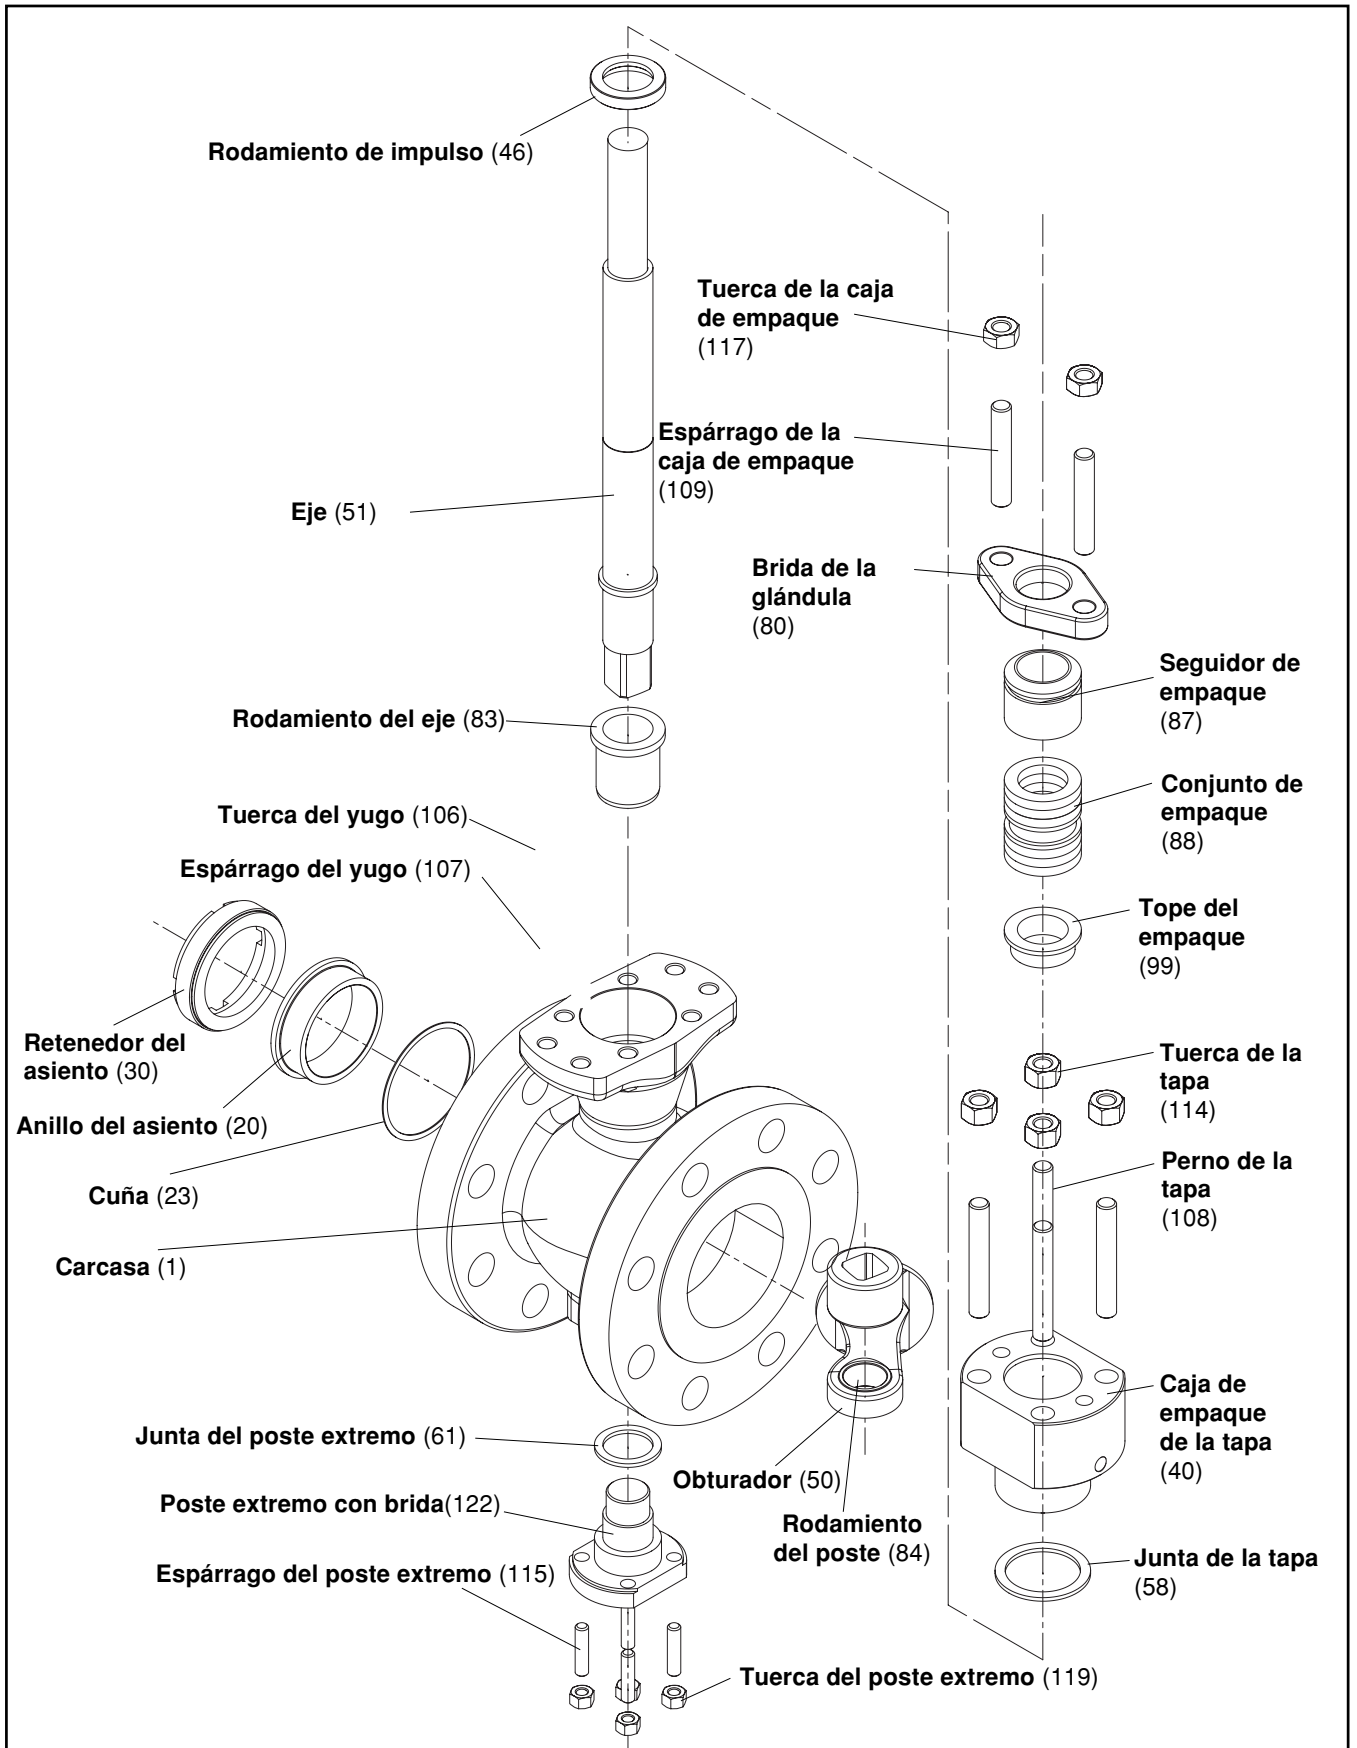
Vista de despiece del subconjunto de la carcasa de MaxFlo 3
